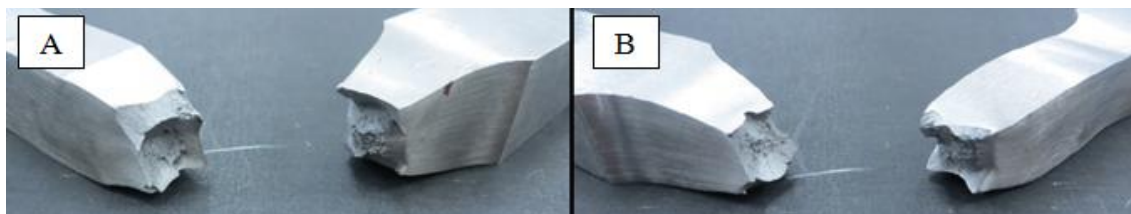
Ensaio de tracção - Superfície da fractura nos provetes soldados pelo fio
